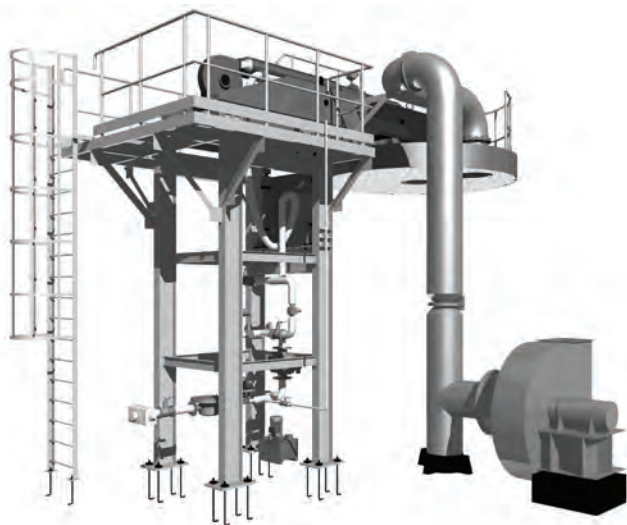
Вертикальная установка сушки и разогрева футеровки сталеразливочных ковшей
